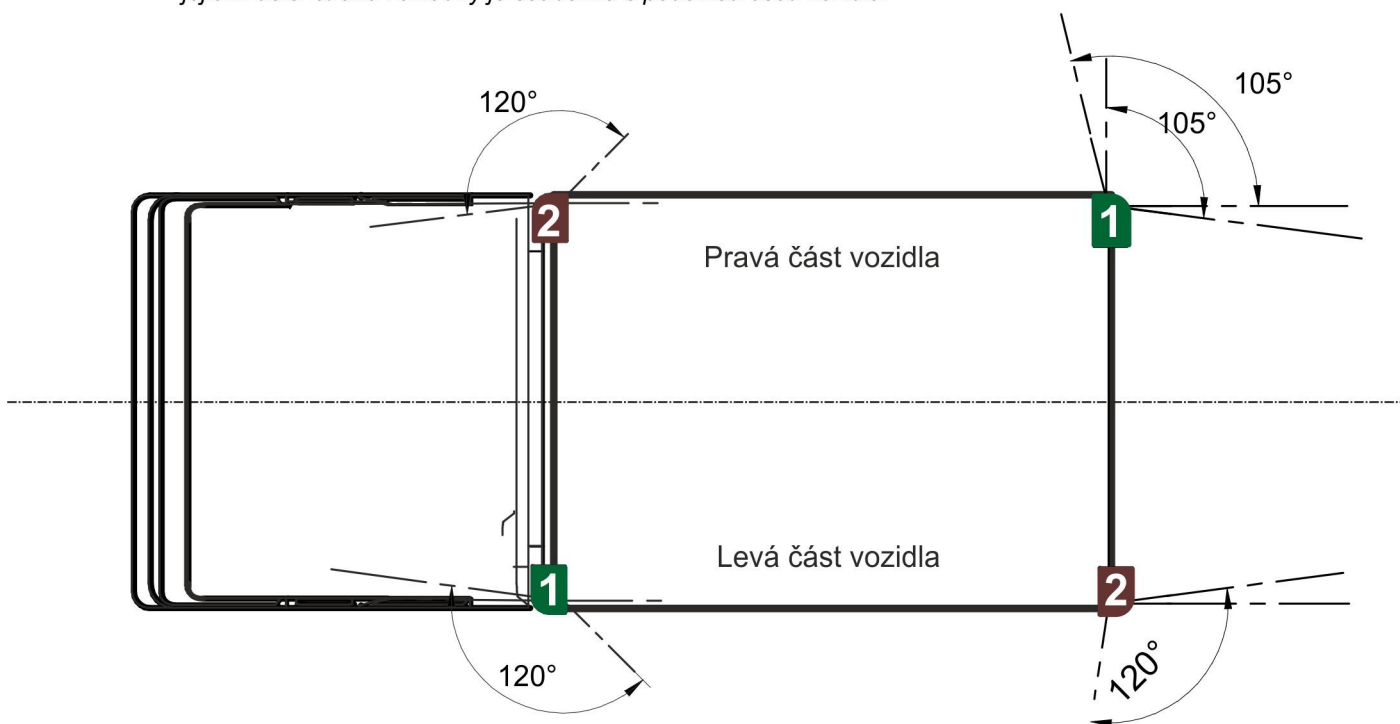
Varianta A - montáž při použití světelné soupravy a dvou zadních rohových světil LED x 44-II, jejichž delší strana základny je kolmá na podélnou osu vozidla.
